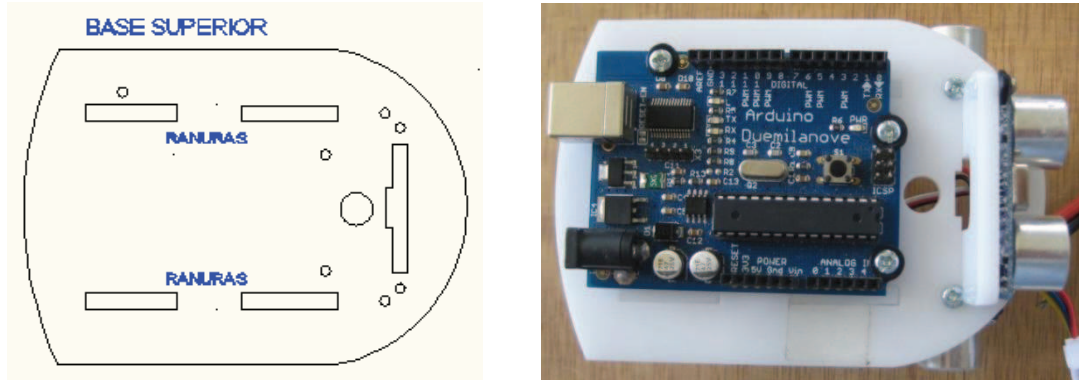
Izquierda) Base3 dibujada en AUTOCAD, derecha) Base3 ensamblada vista superior
